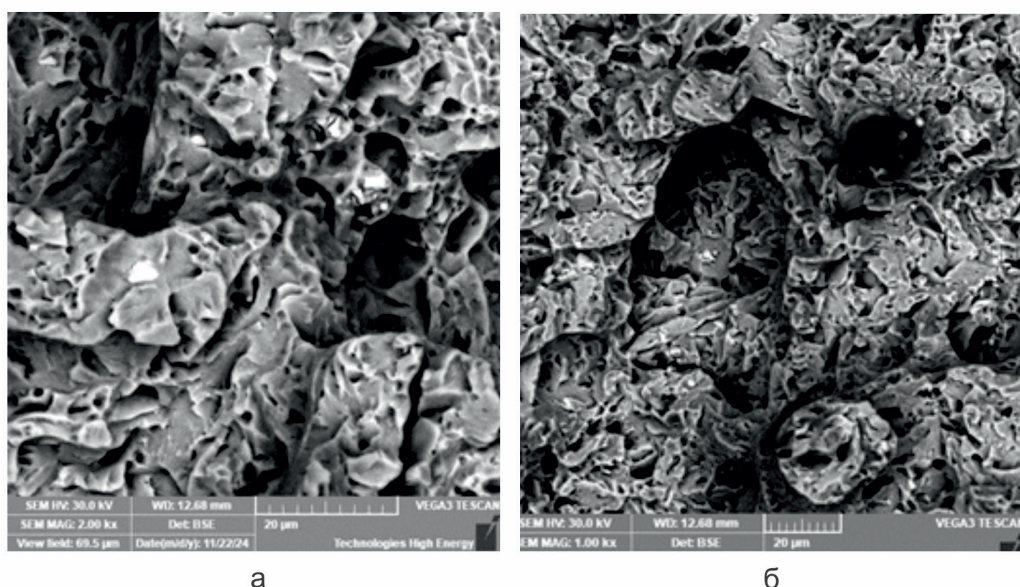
Фрактографія поверхні руйнування зразка поковки сталі типу 3Х3М3.
